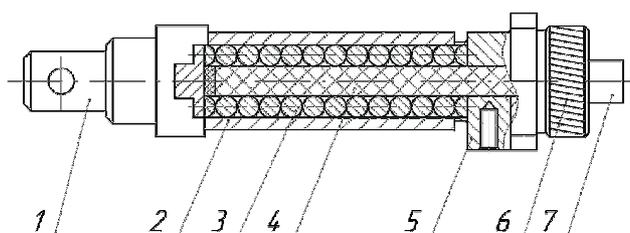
Внешний вид и устройство механизма раскрытия аэродинамической поверхности
